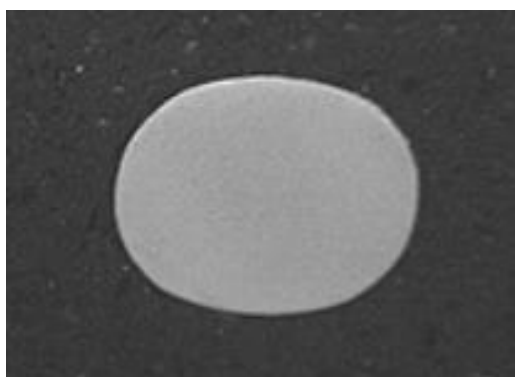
Corte de seção transversal de fio máquina com dimensões fora de tolerância. Fonte: LIMA, 2012.
